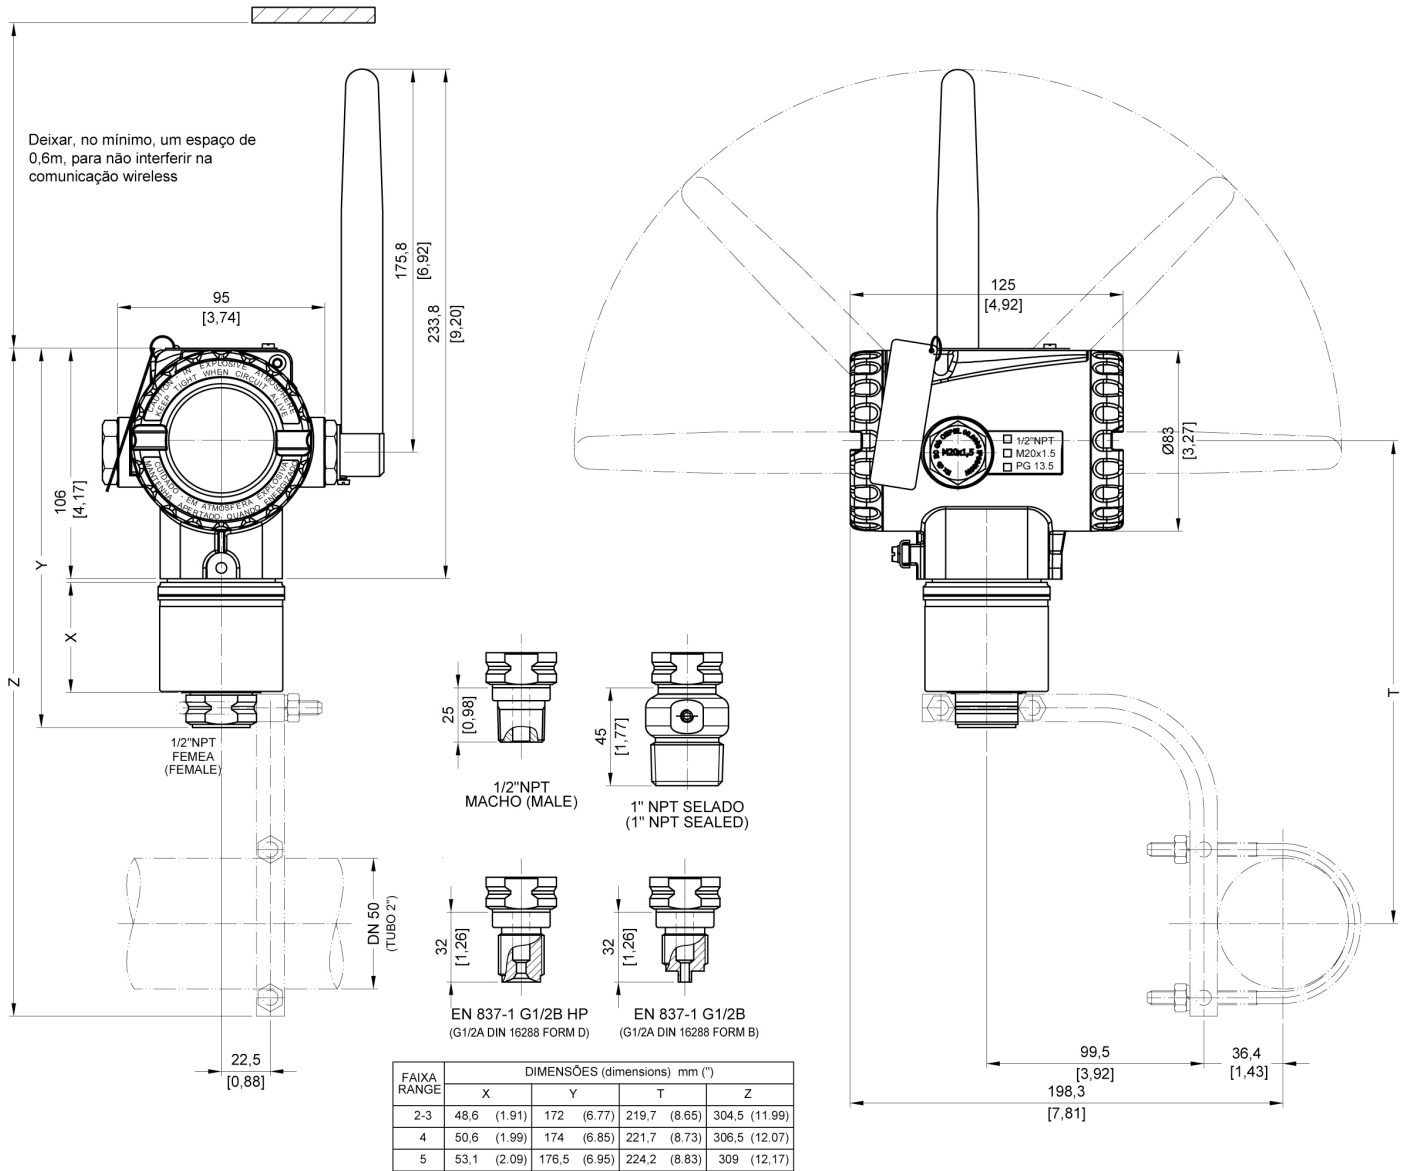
(f) – Des. Dimensional de Montagem LD400 WirelessHART™ - Transmissor de Pressão Manométrica Inline
